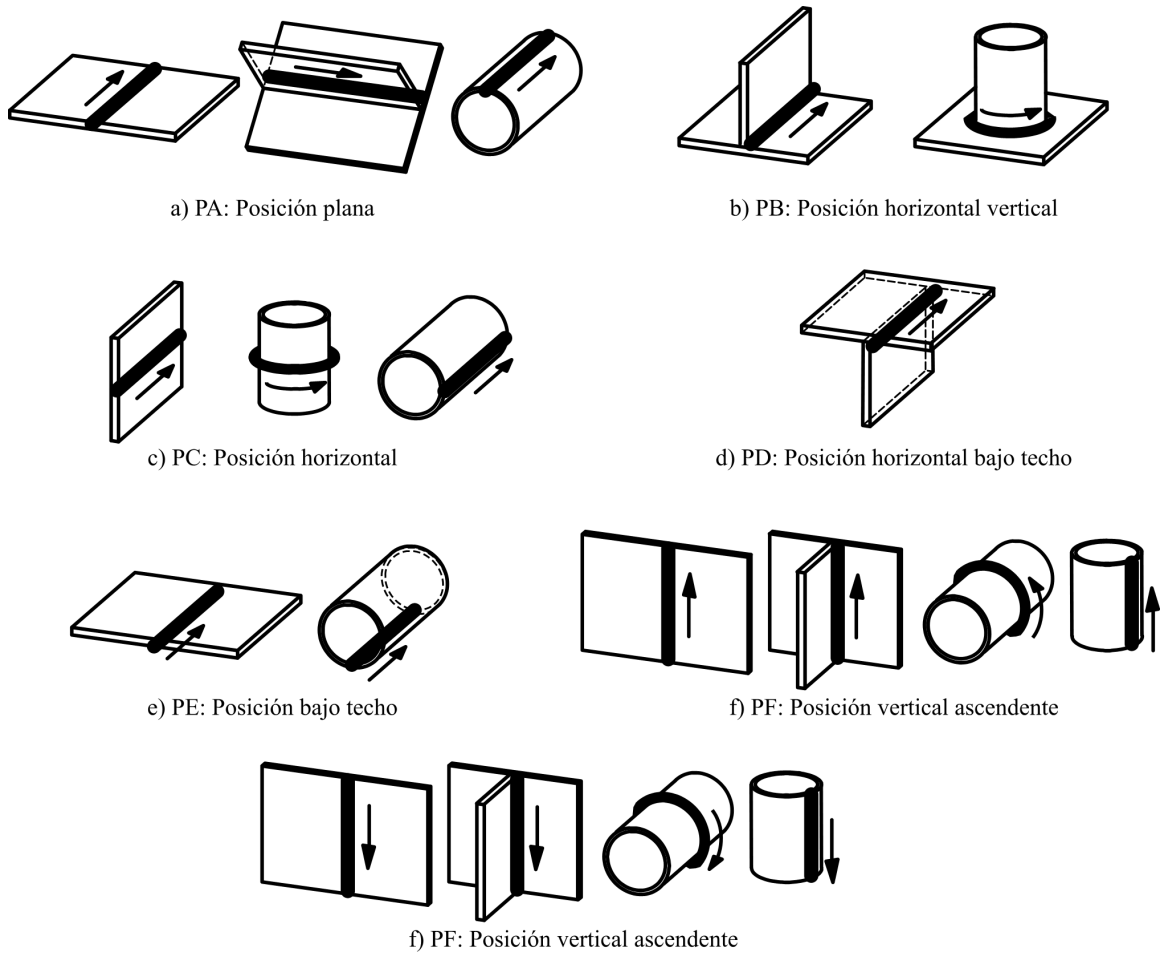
Ejemplos de posiciones principales de soldadura (NC-ISO 6947: 2004)
